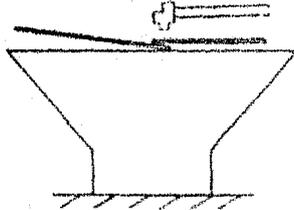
b = Soldadura homogénea por forja y martillo.
